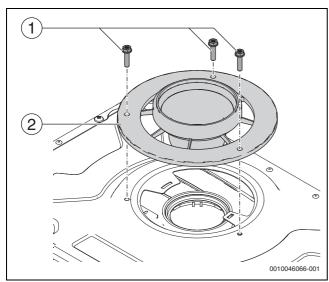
Monter le set du conduit de fumées et l'adaptateur du conduit de fumées
